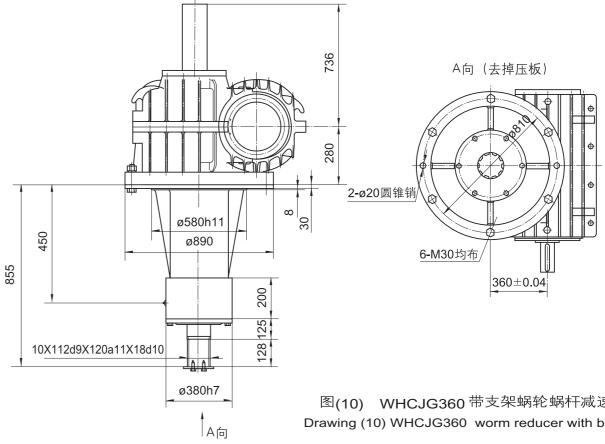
WHCJ360 带支架蜗轮蜗杆减速机 Drawing 10 WHCJ360 worm reducer with bracket
